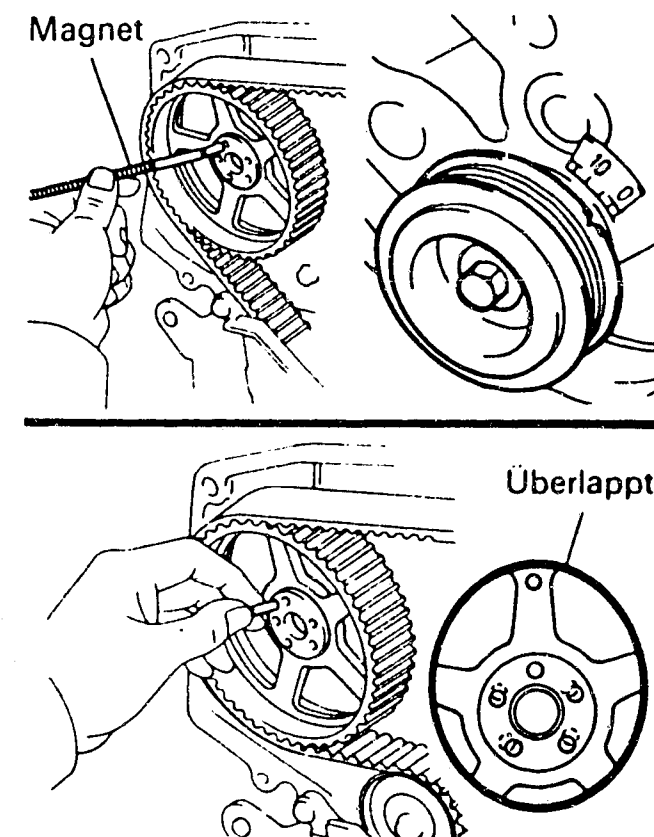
Motor 3S-GE: Feineinstellung der Motorsteuerung. Oben: Der Fixierstift lässt sich mit einem Magneten aus der Bohrung ziehen. – Unten: Durch Verschieben des Nockenwellenrads gegenüber dem Flansch lassen sich die Steuerzeiten sehr genau einstellen.
